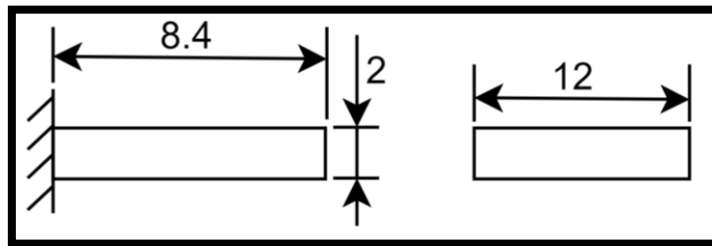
Apoyo y dimensiones de la cuchilla de corte.
